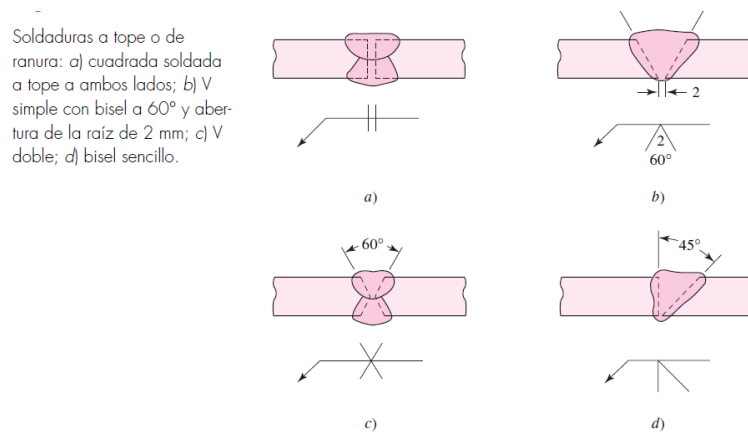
Tipos de cordones de soldadura a tope. Fuente: Budynas, Richard G.; Nisbett, J. Keith, pág.460 [31].
